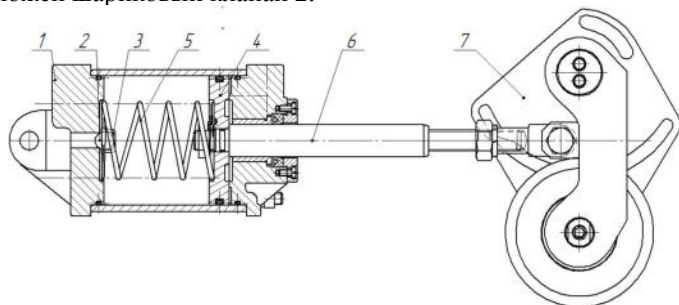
Схема пневмомеханическое устройства для натяжения
